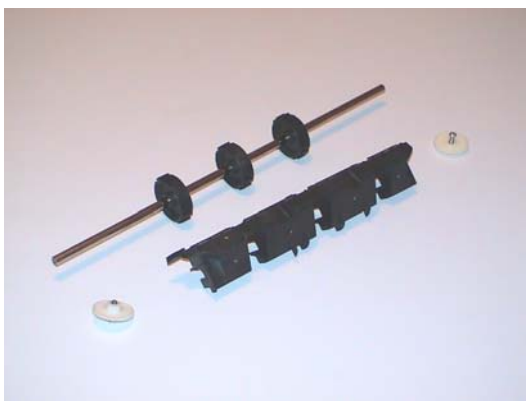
Eje horizontal desmontado de la pieza base que lo permitirá girar
